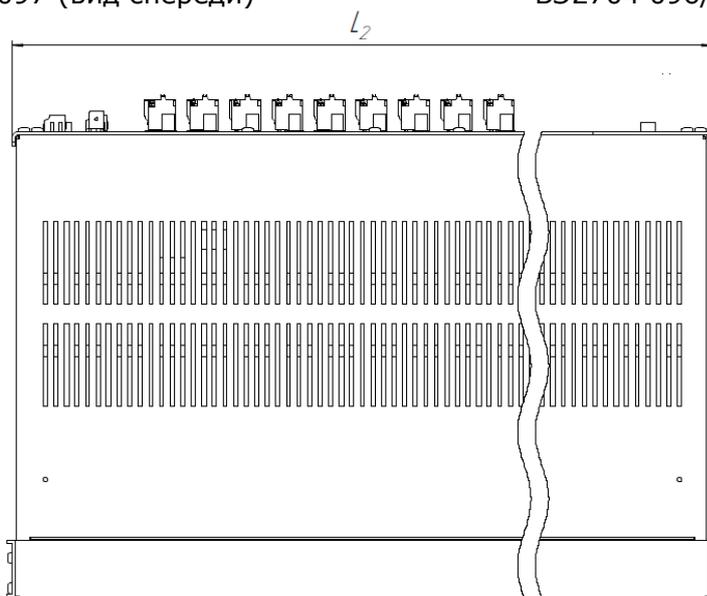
Габаритные и установочные размеры терминала БЭ2704 096/097 (вид сверху)
